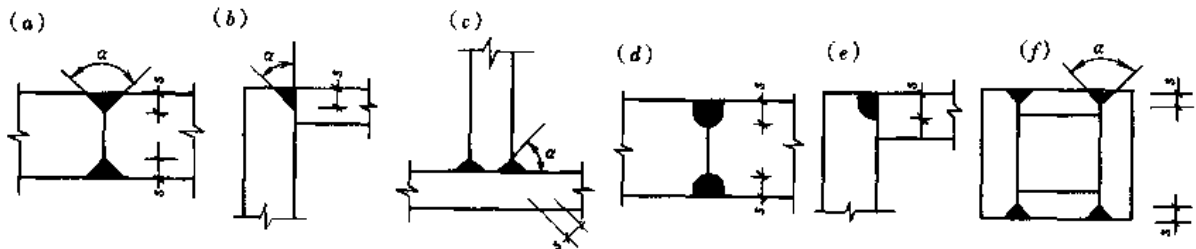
部分焊透的对接焊缝和其与角焊缝的组合焊缝截面
